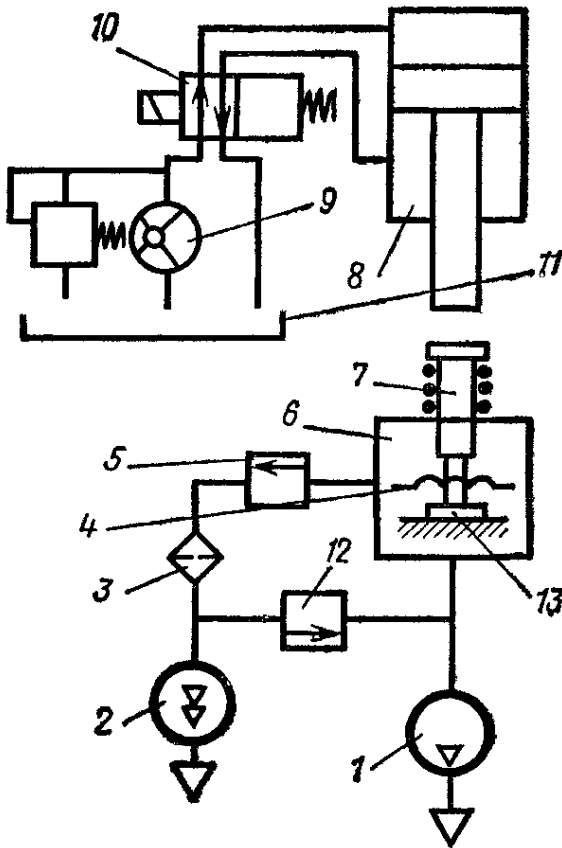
Схема установки для диффузионной сварки с индукционным нагревом деталей
